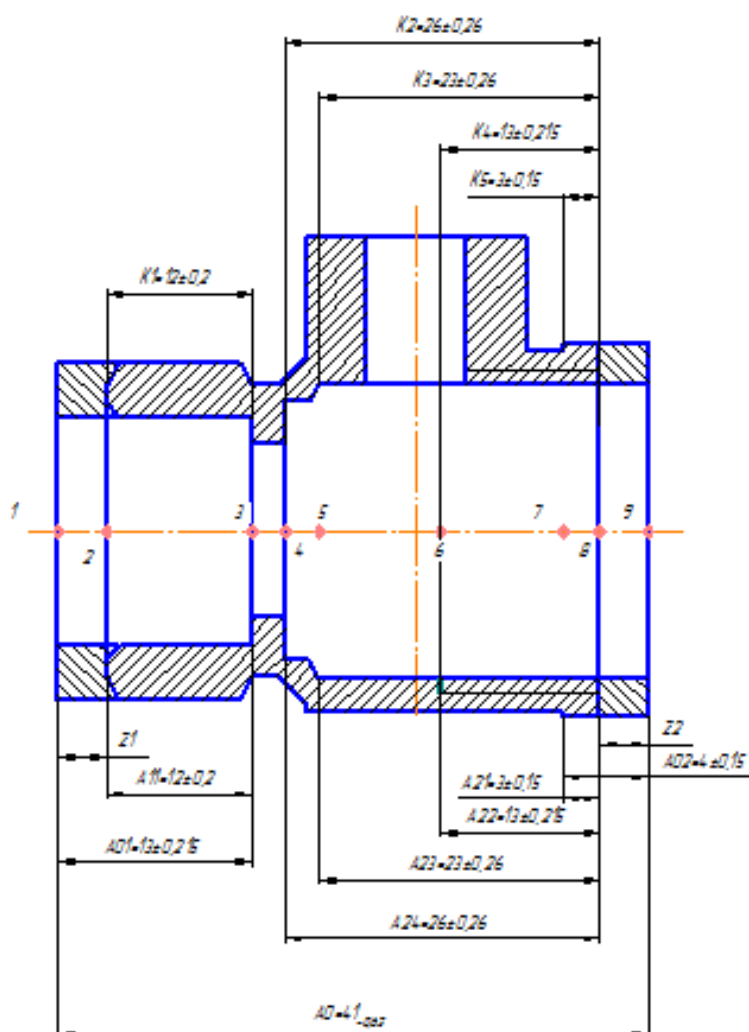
Размерная схема технологического процесса изготовления корпуса
